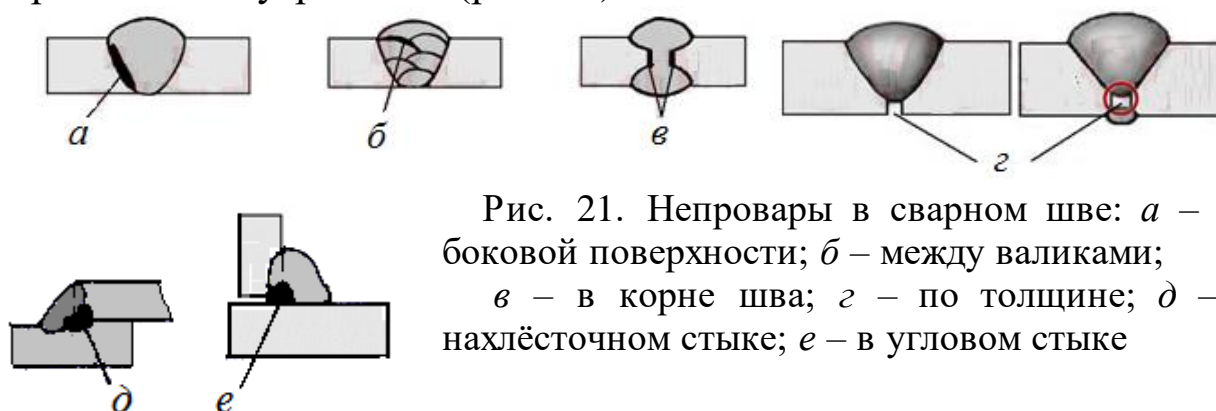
Непровары в сварном шве: *a* – по боковой поверхности; *б* – между валиками; *в* – в корне шва; *г* – по толщине; *д* – в нахлесточном стыке; *е* – в угловом стыке
